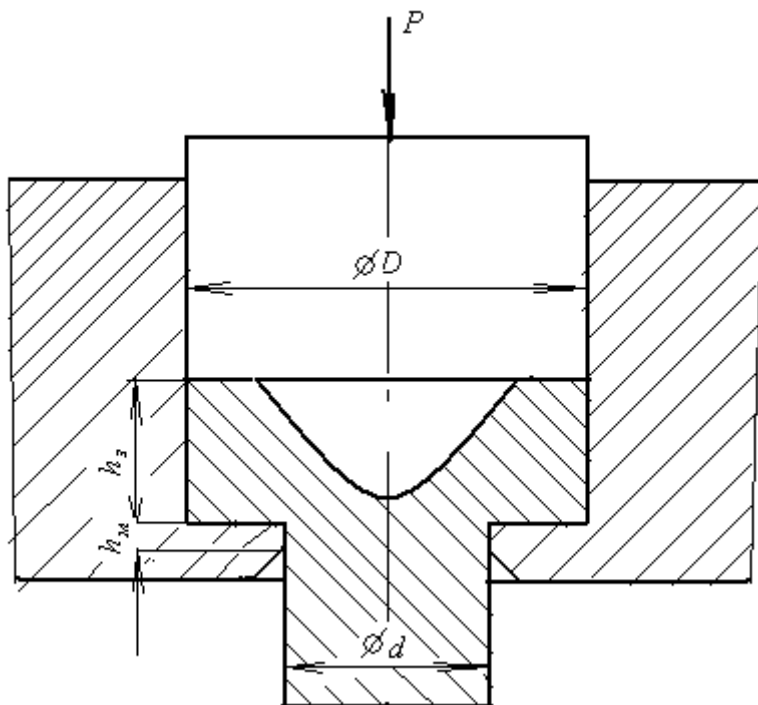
Схема выдавливания заготовки типа «вал с фланцем»
